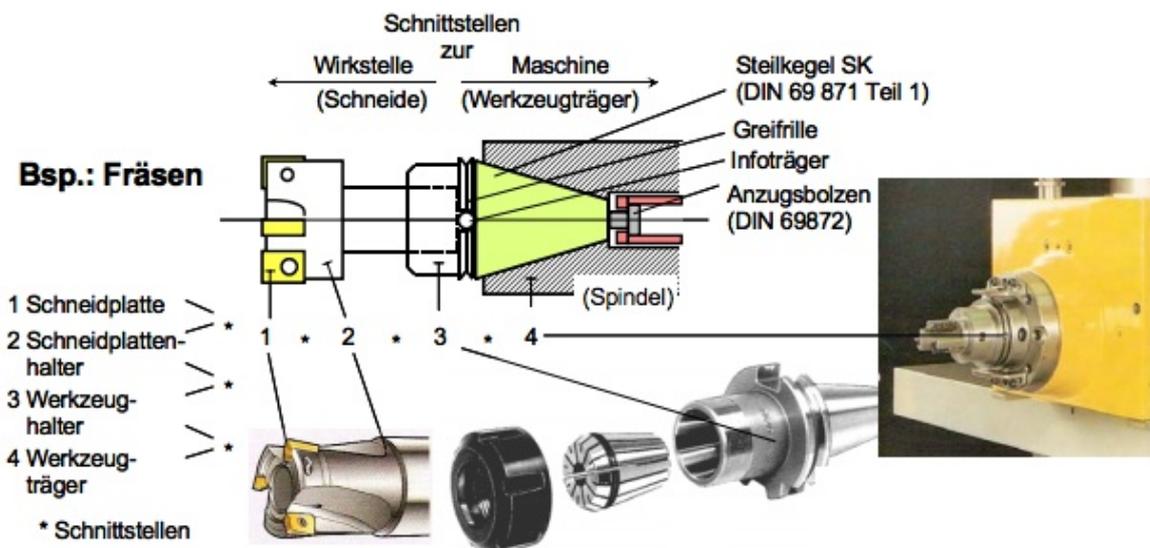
Komponenten eines Werkzeugsystems [2]
